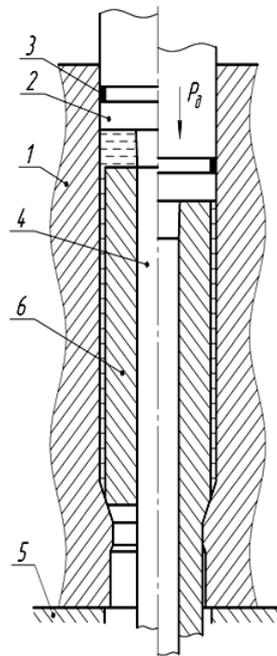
Схема гидропрессования трубчатых заготовок на оправке
